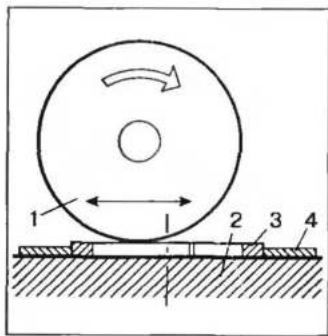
Схема шлифования торцев кольца на плоскошлифовальном станке: 1 — шлифовальный круг; 2 — магнитный стол; 3 — кольцо; 4 — оправка
